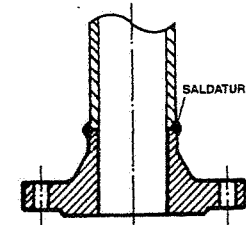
Modalità di giunzione mediante saldatura fra tubo e flangia a collare.
